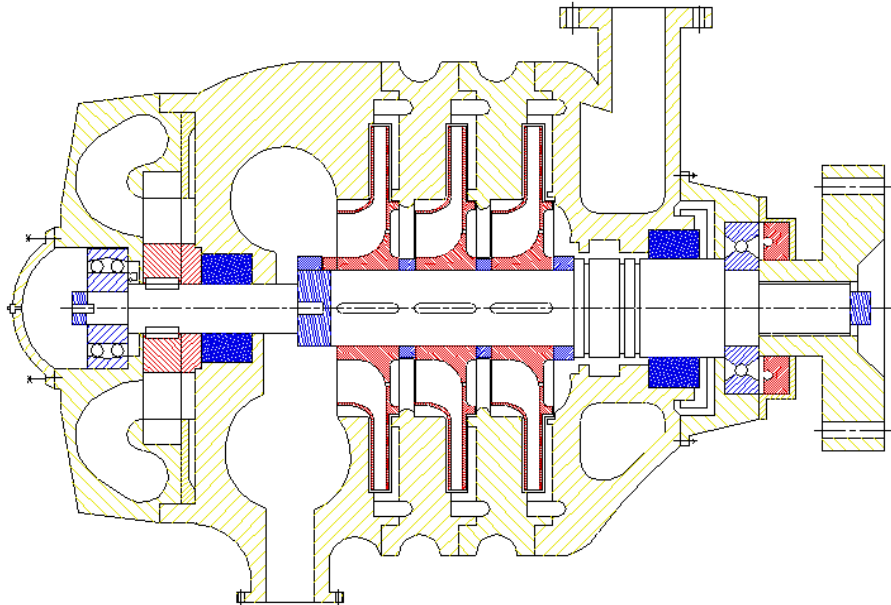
Disposición de los apoyos y empaquetaduras en la bomba centrífuga multietápica con difusores objeto de estudio.
